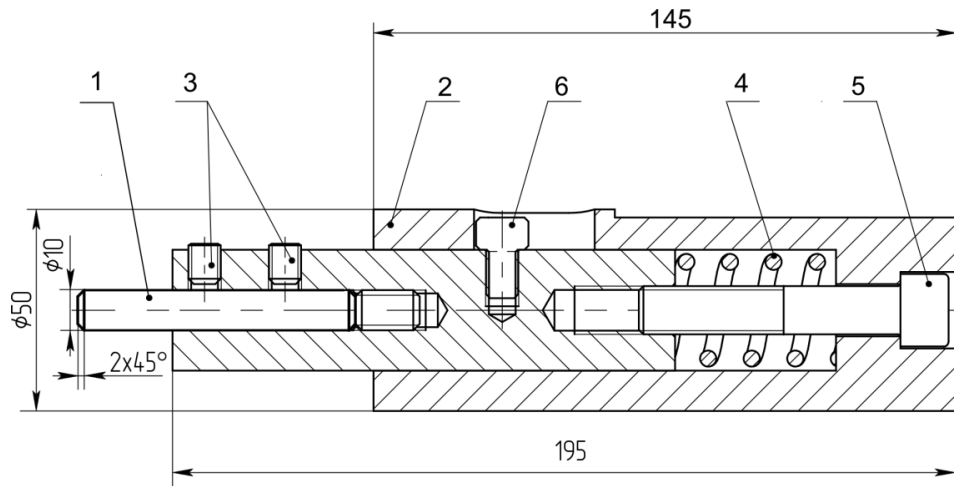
Державка цилиндрического инструмента для реализации поверхностной заковки в процессе обработки трением с перемешиванием на станках с ЧПУ
